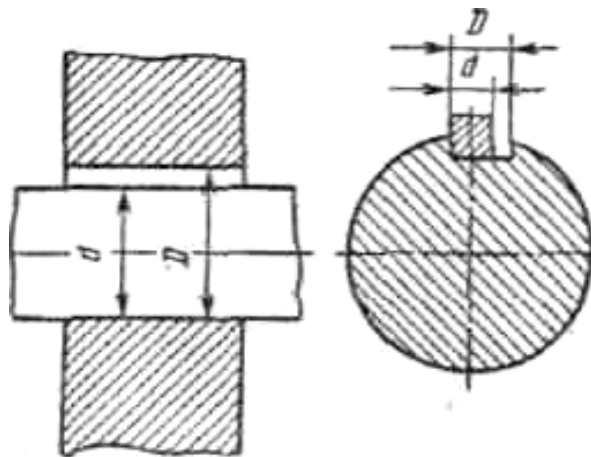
Примеры охватываемой и охватывающей поверхностей
